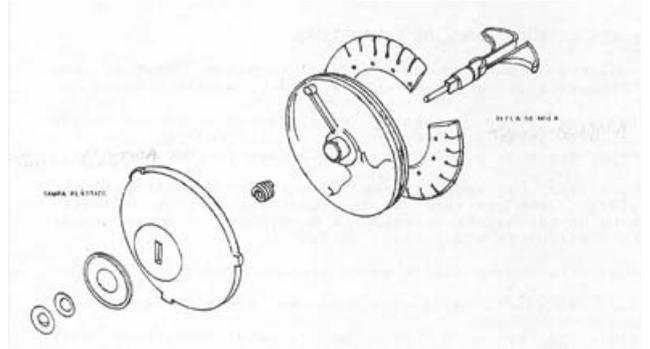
Vista explodida de uma tampa do bujão de abastecimento
